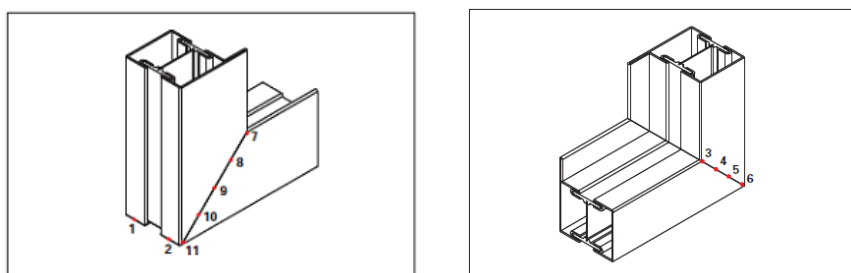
Soldadura de los perfiles de acero inoxidable
